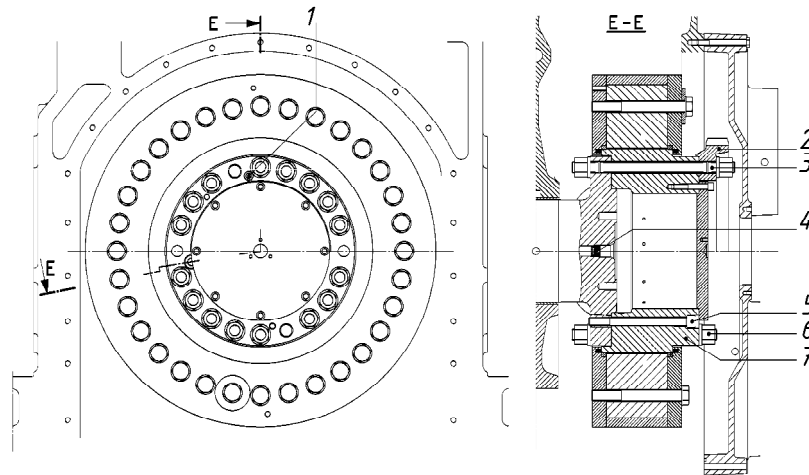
Демпфер крутильних коливань сухого тертя: 1 – штифт; 2 – шестерня приводу насосів; 3 – шпильки кріплення маточини; 4 – центрувальний отвір; 5 – бовти кріплення корпусу демпферу; 6 – гайки кріплення; 7 – маточина демпферу
